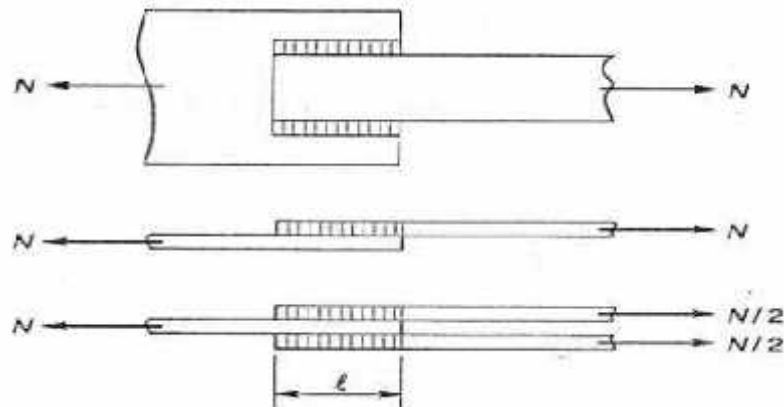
Schéma représentatif de l'assemblage par soudure
